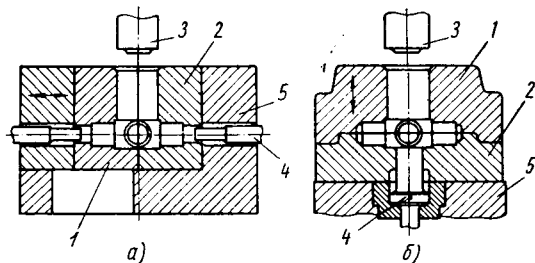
Схемы штамповки поковки типа крестовины в штампе: а — с вертикальным разъемом матриц; б — с горизонтальным разъемом матриц.
